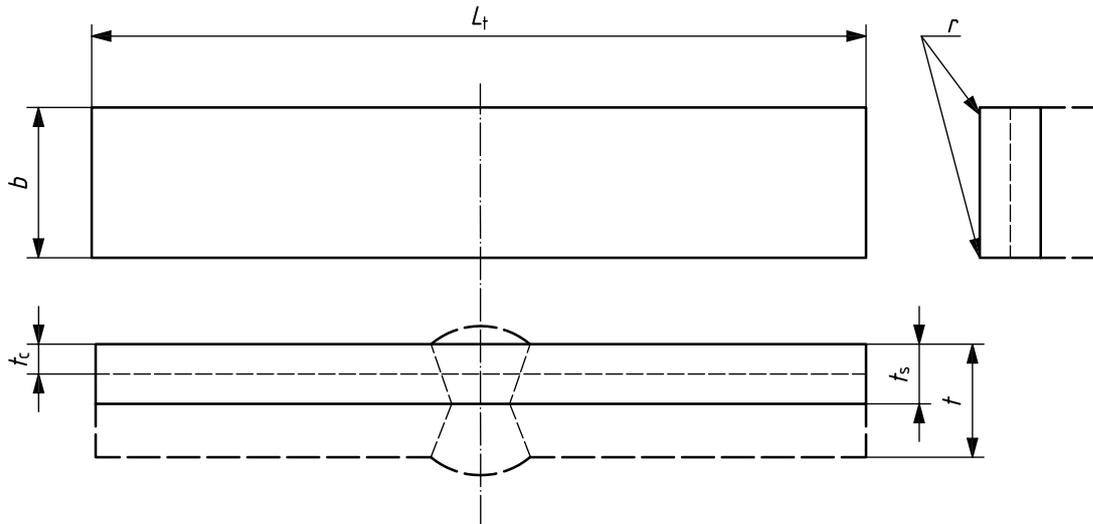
Éprouvette de pliage endroit sur revêtement sur soudure bout à bout (FBCB)
